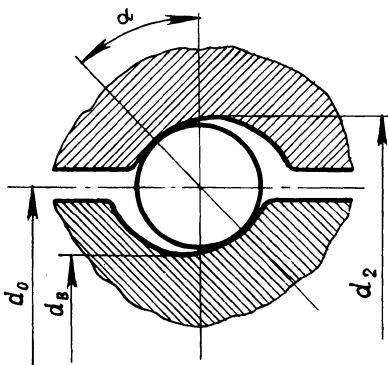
Контакт шарика с рабочими поверхностями резьбы винта и гайки
